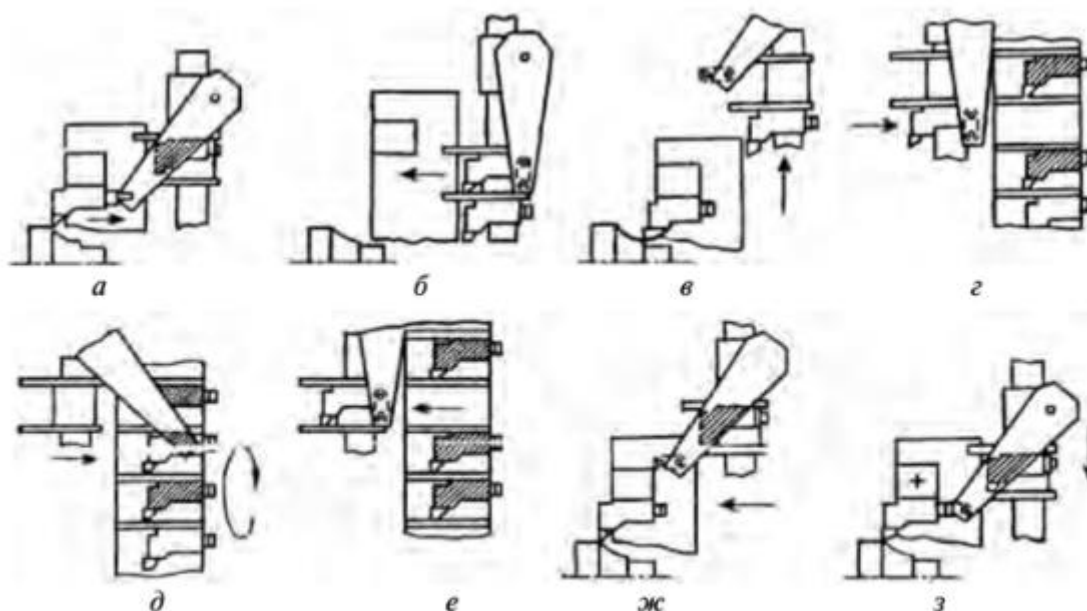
Цикл работы (а — з) автооператора для автоматической смены инструмента из магазина барабанного типа на токарном станке
